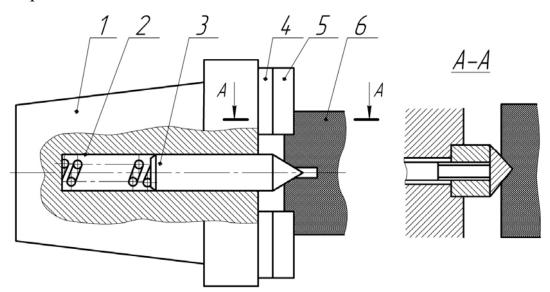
Поводковый патрон с торцовыми ножами: 1 – корпус; 2 – пружина; 3 – центр; 4 – торцовый упор; 5 – нож упора из твердого сплава; 6 – обрабатываемая заготовка
